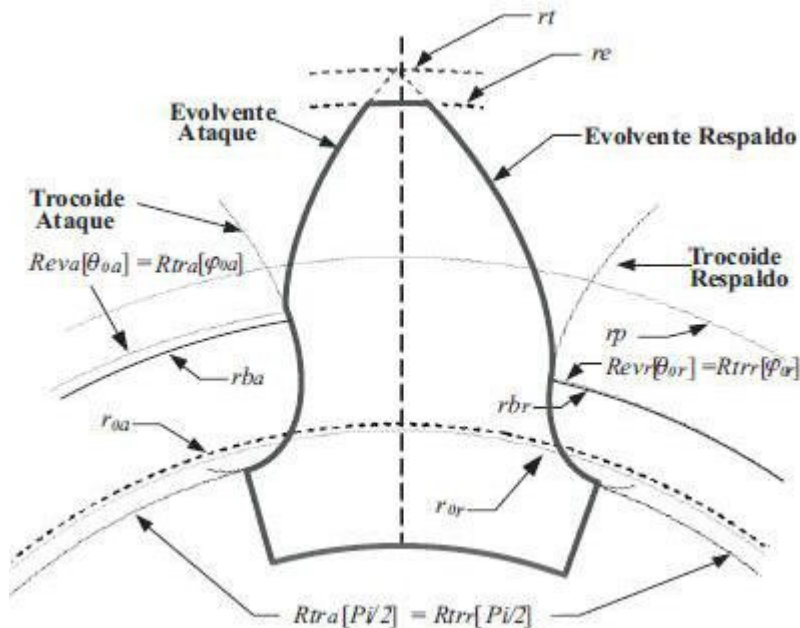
Diente de engranaje asimétrico [F-4]
